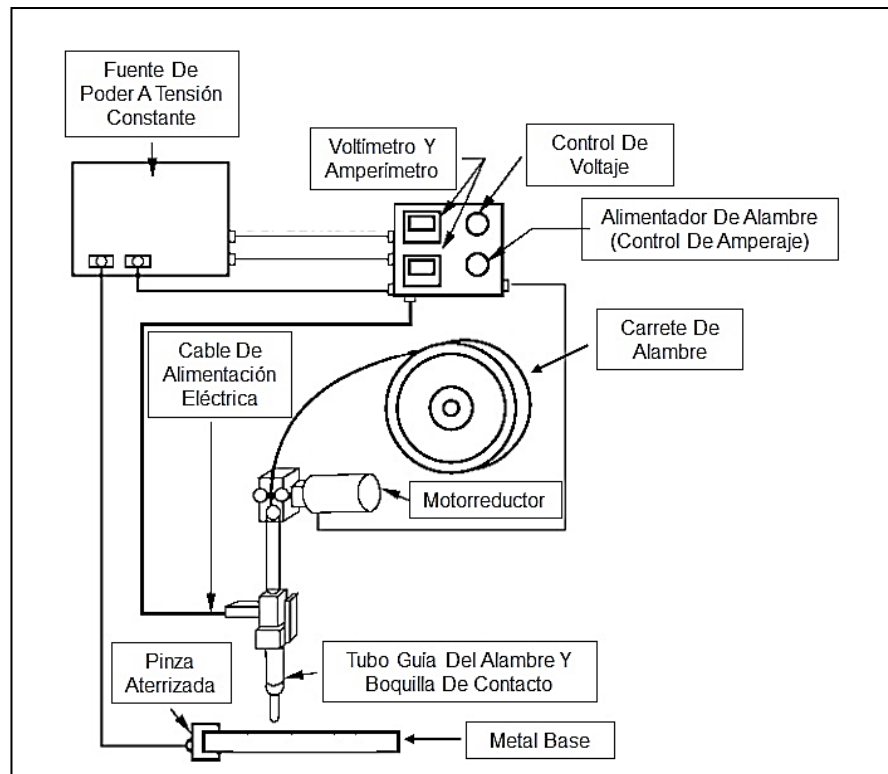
Esquema Del Circuito Del Proceso De Soldadura Por Arco Con Alambre Tubular [5].
